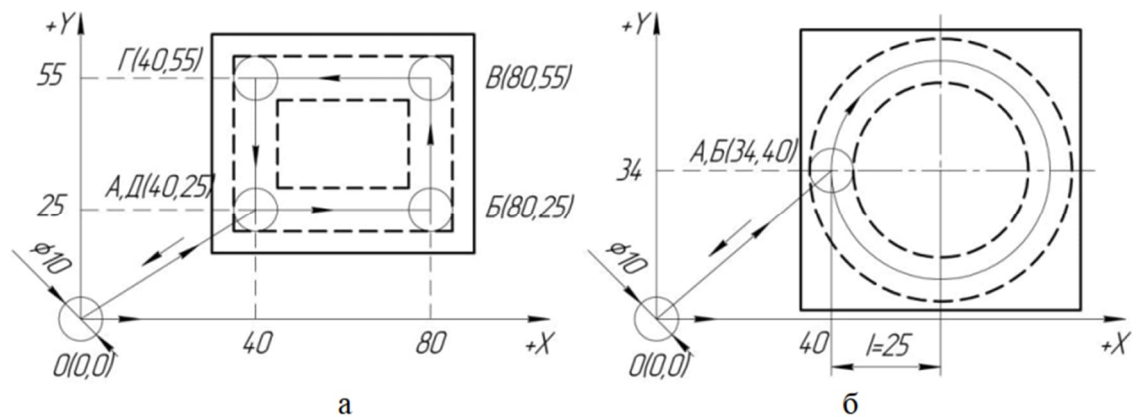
Фрезерування канавки по прямій (а) і по колу (б)
